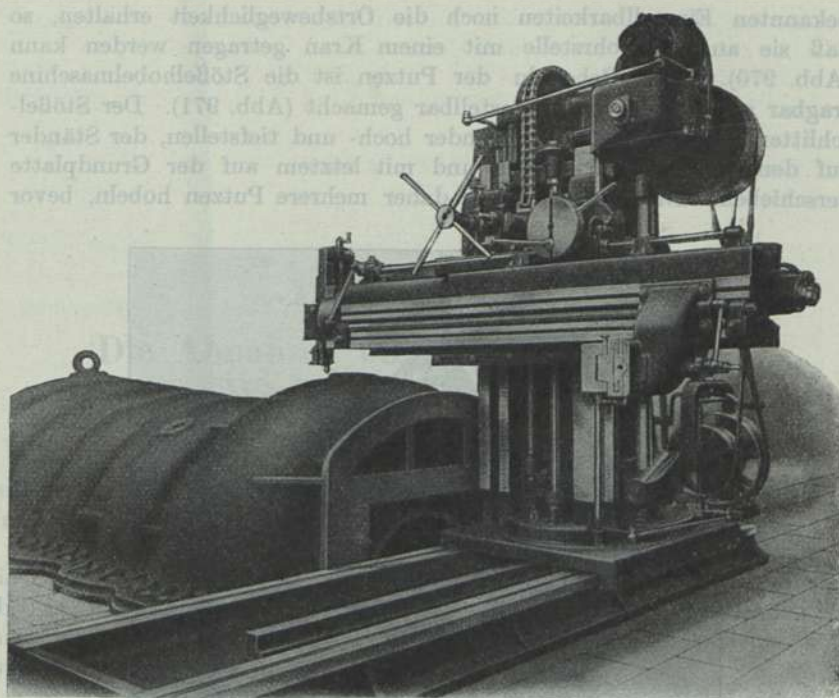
Tragbare Hobelmaschine. Collet & Engelhard, Offenbach a/M.
